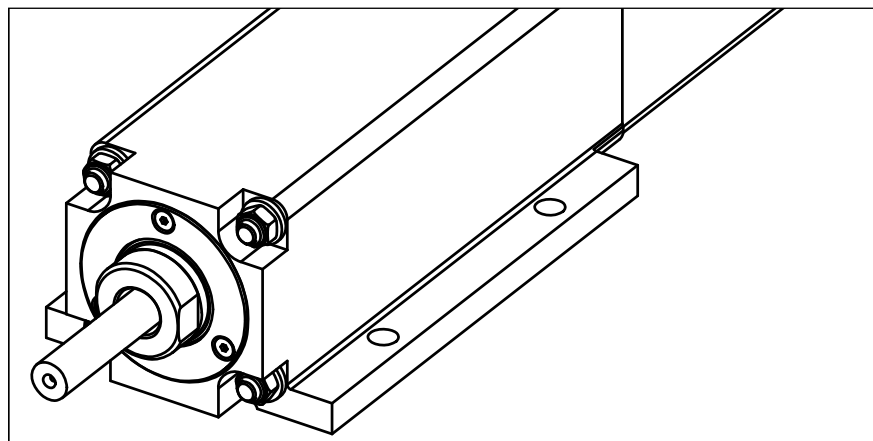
O projeto do GSWA33 Guiado inclui esta montagem, que tem as seguintes funções: dispositivo anti-rotação, dispositivo de montagem e apoio para carga lateral.
